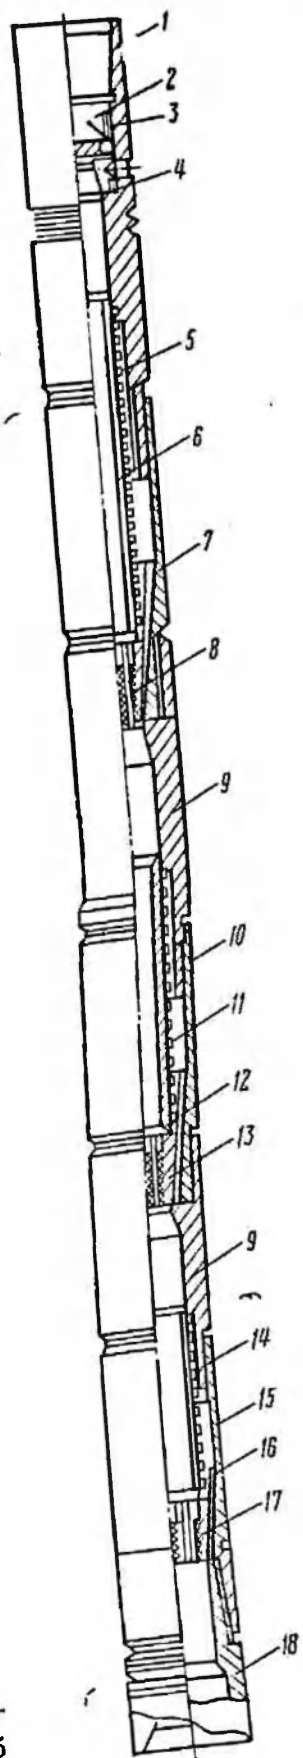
Комбинированный ловитель штанг и труб ЛКШТ-168
